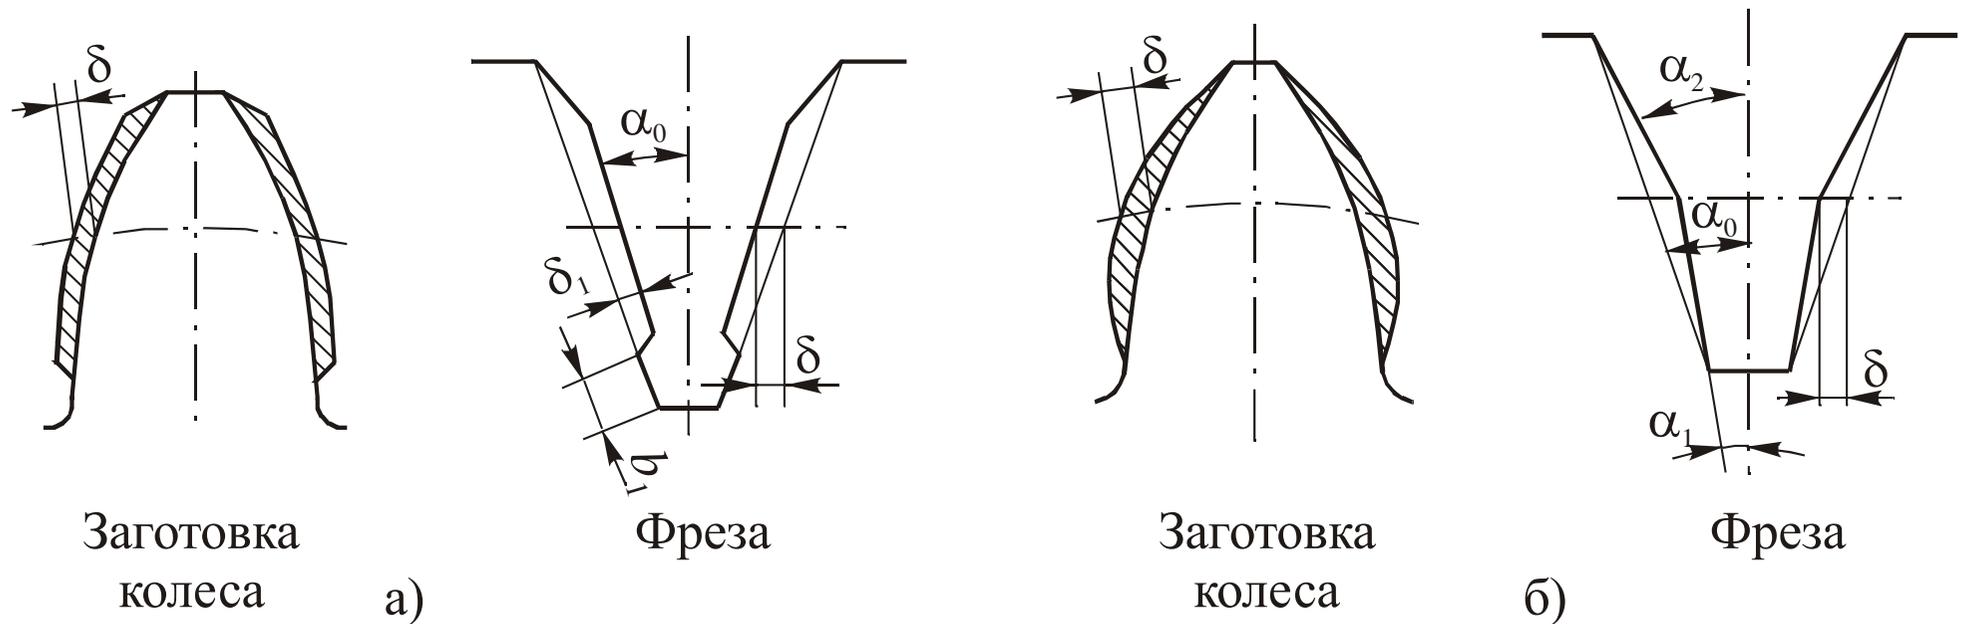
Припуск под шевингование и формы зубьев инструментов для нарезания зубьев колес под шевингование червячной фрезой:
